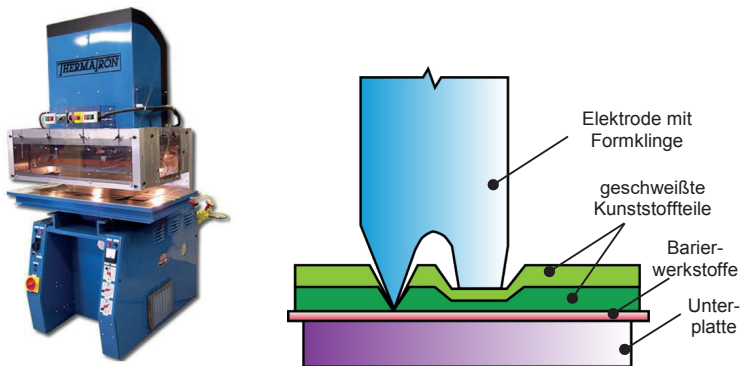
Anlage für Hochfrequenzschweißen
